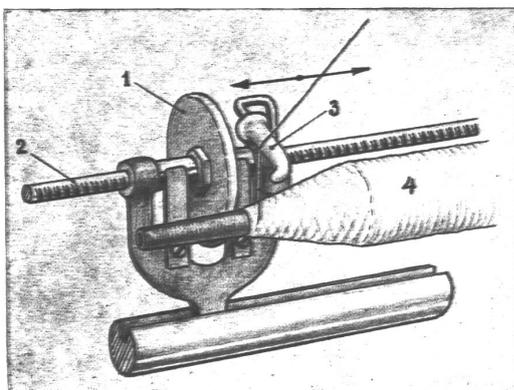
Selbstschaltendes Fühlerrädchen von der Maschinenfabrik Schweiter A.-G., Horgen.
